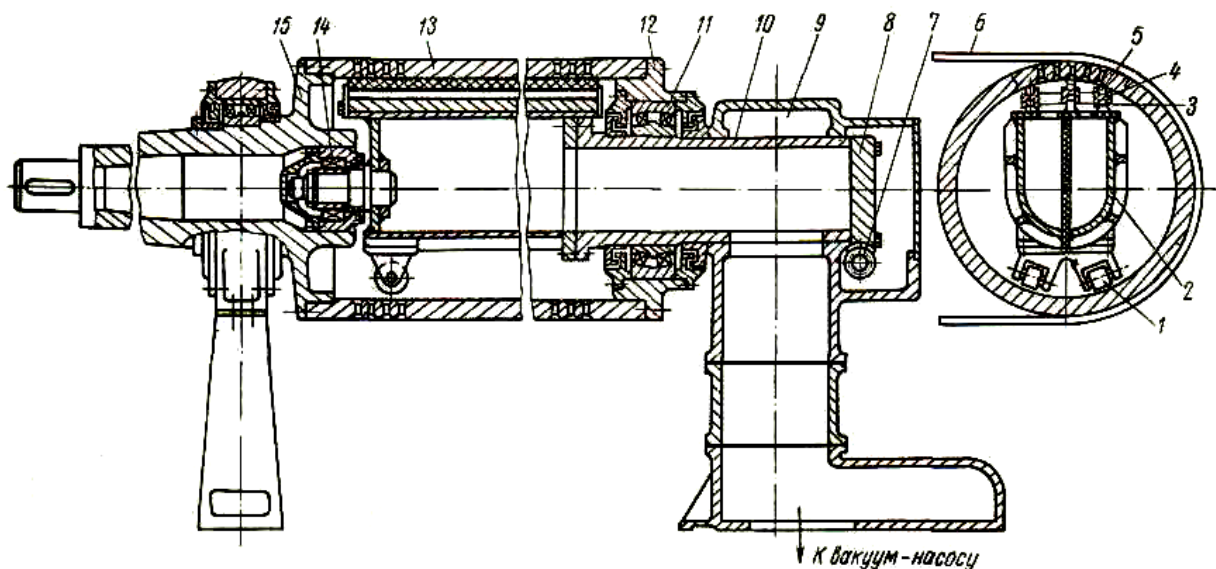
Двухкамерный гауч-вал: 1- обрешиненные ролики; 2 – вакуумная камера; 3 – резиновая пневмокамера для прижима уплотнений к рубашке; 4 – стальная рамка для установки уплотнений; 5 – графитовые уплотнения; 6 – сетка; 7 – червяк; 8 – сектор червячной пары; 9 – канал для удаления мокровоздушной смеси; 10 – полая цапфа; 11 – подшипник; 12 – крышка; 13 – перфорированная вращающаяся рубашка; 14 – подшипник, удерживающий отсасывающую камеру в приводной цапфе; 15 – приводная цапфа
